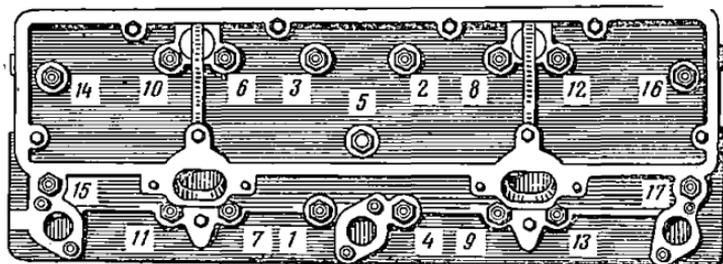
Очередность затяжки крепления головки цилиндров двигателя СМД-14.
